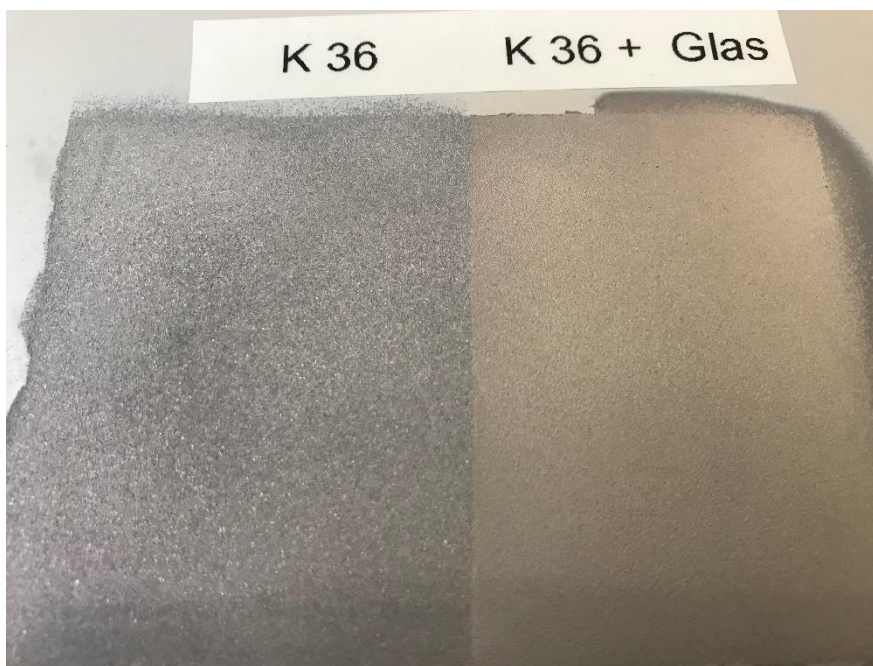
Es wurde sich entschieden, das komplette Werkzeug mit der Oberfläche K36 auszustatten
